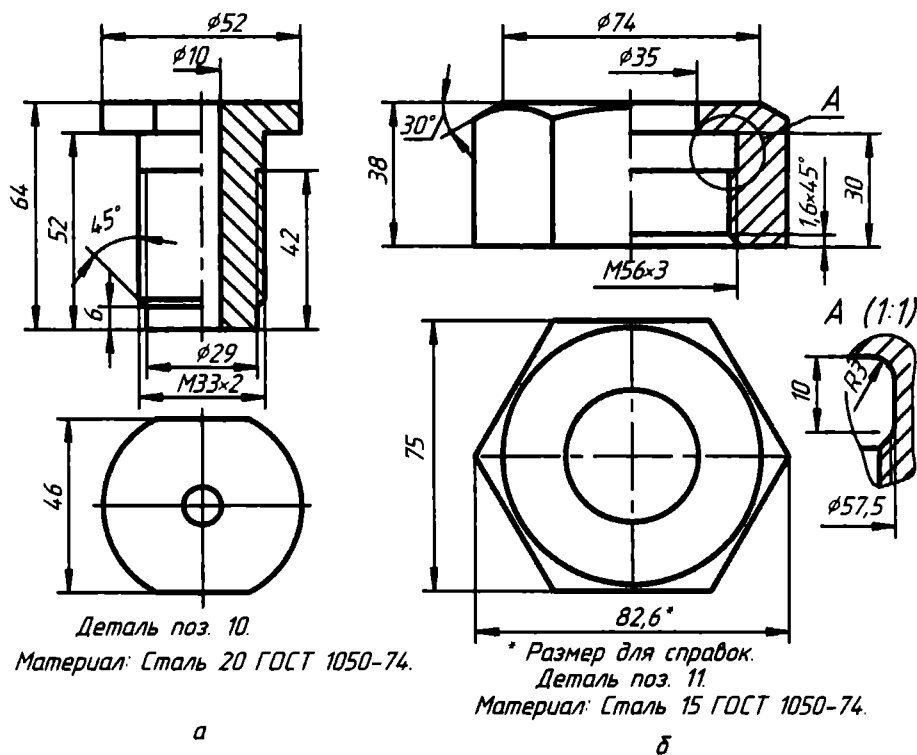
Чертежи: а — ниппеля; б — гайки
